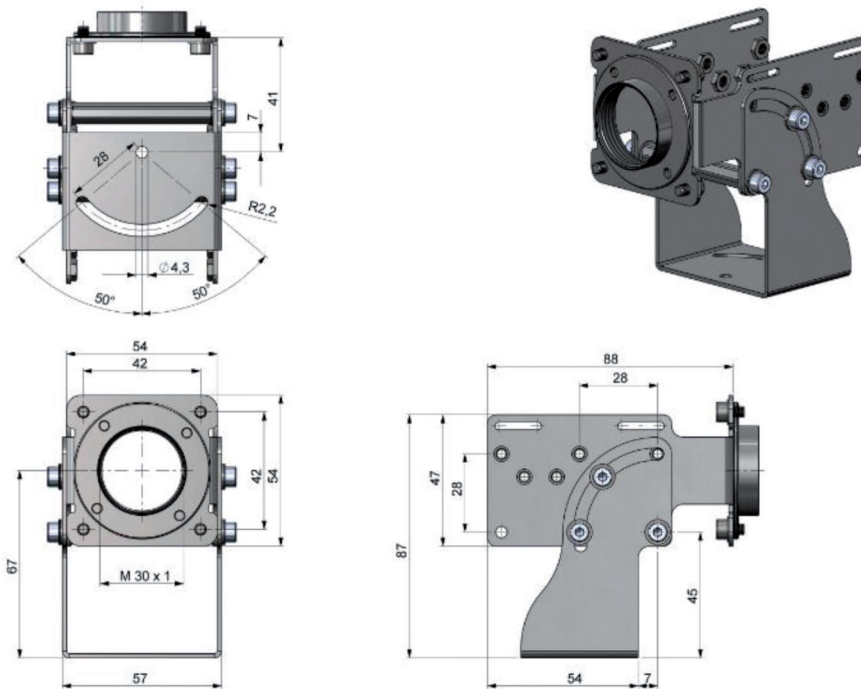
Montagewinkel TM-APLAB, Abmessungen in mm
